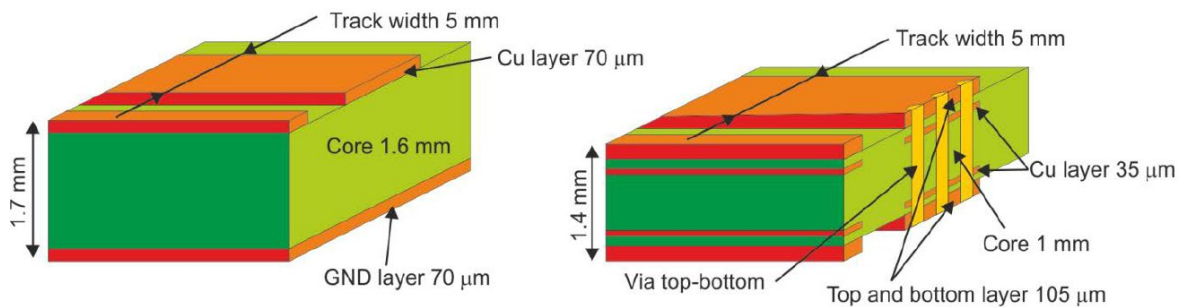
Estructura del PCB original (izquierda) y final (derecha)
